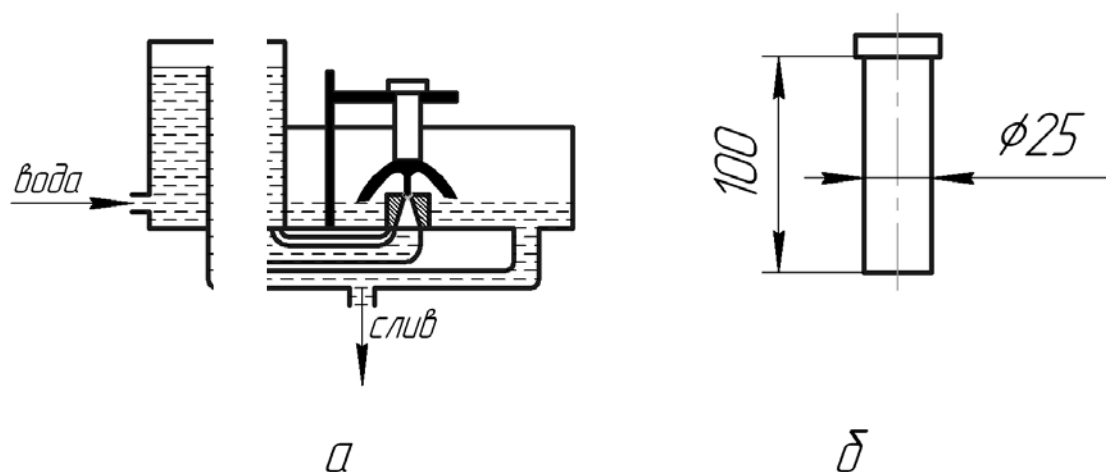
Установка (а) и образец (б) для торцевой закалки
